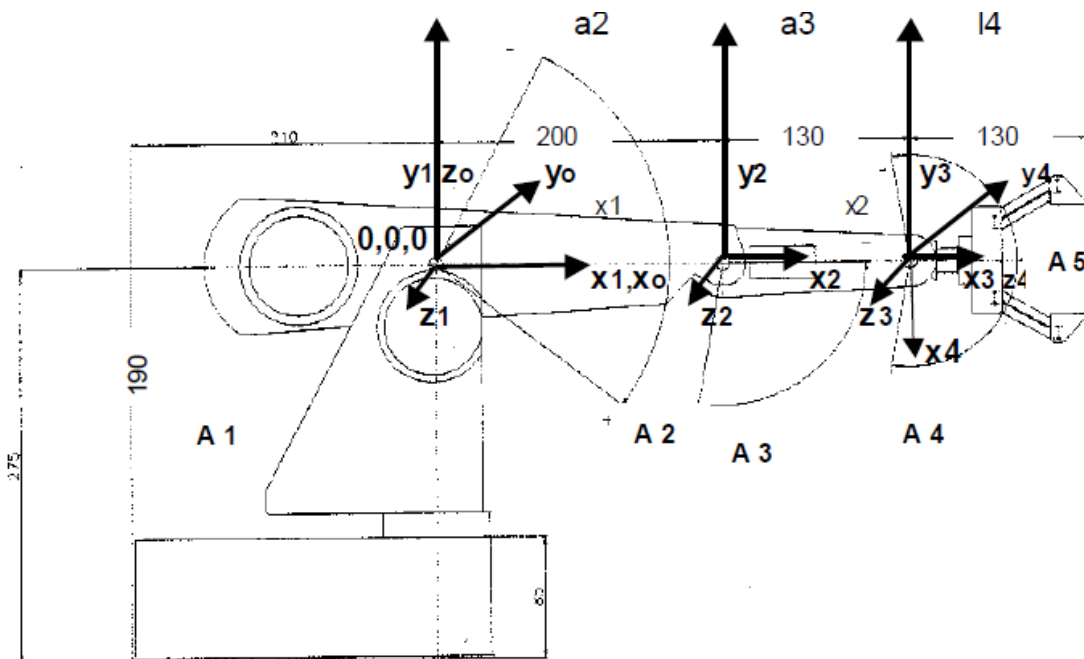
Les dimensions du robot ROB3(vue de face)
